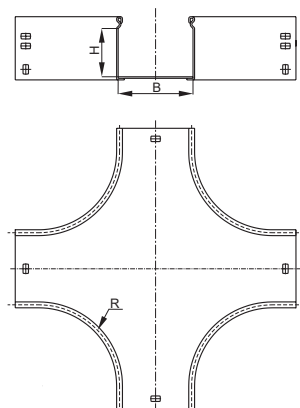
крестовина плавная тип Г01. Размеры для размещения кабеля / Figure C.2 – Smooth crossover of Г01 type. Dimensions for cable placement
